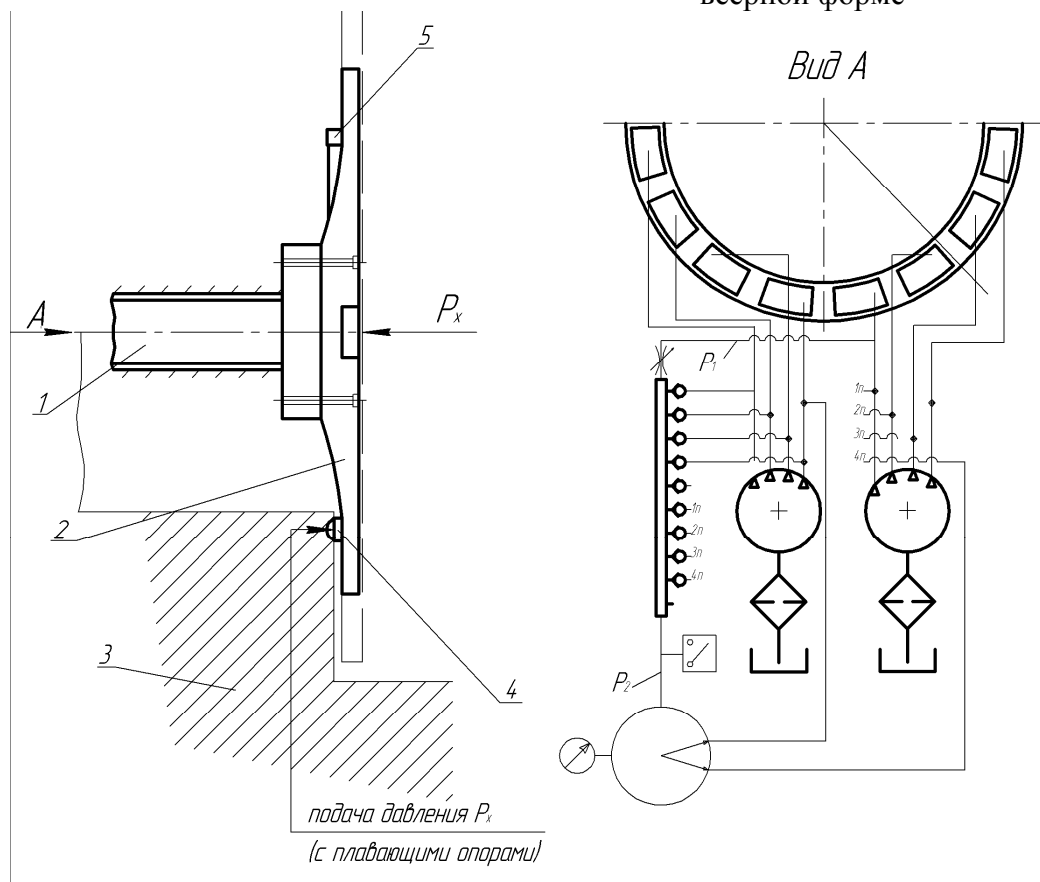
Схема опор планшайбы: 1 – шпиндель с фланцем; 2 – планшайба; 3 - основание; 4 – полукольцевая опора с карманами; 5 – кольцо плоское; P_x – сила резания; вид А – рис. 71,а [6].
